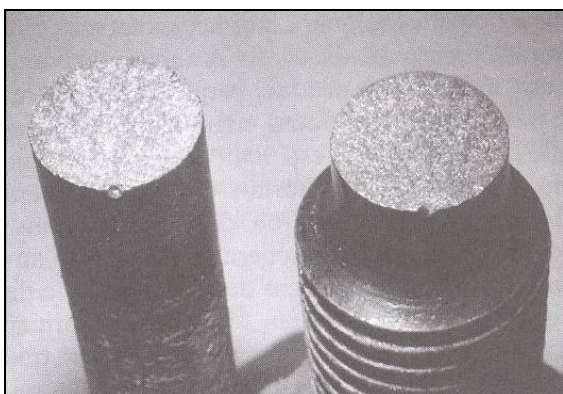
Superfície de fractura de um material frágil (Callister Jr., 2002).
